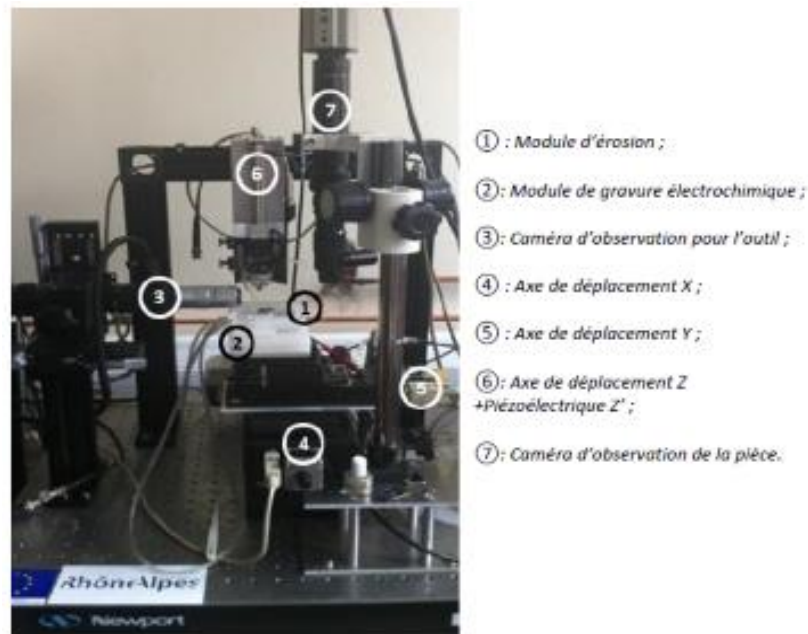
Première génération de machine de micro-usinage par électroérosion [13].
